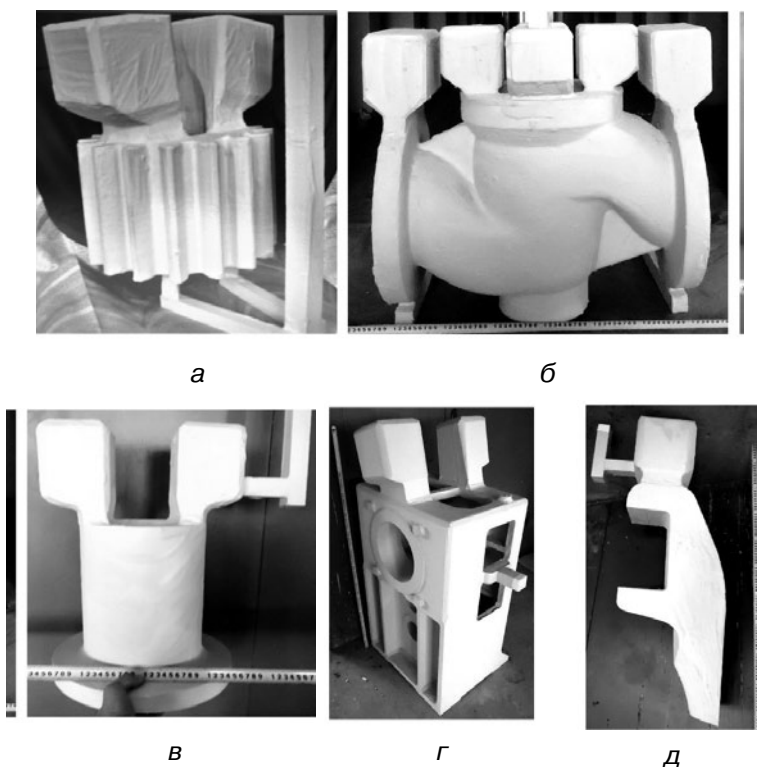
Модели стальных отливок: а – шестерни; б – задвижки; в – патрубка; г, д – корпусных отливок
